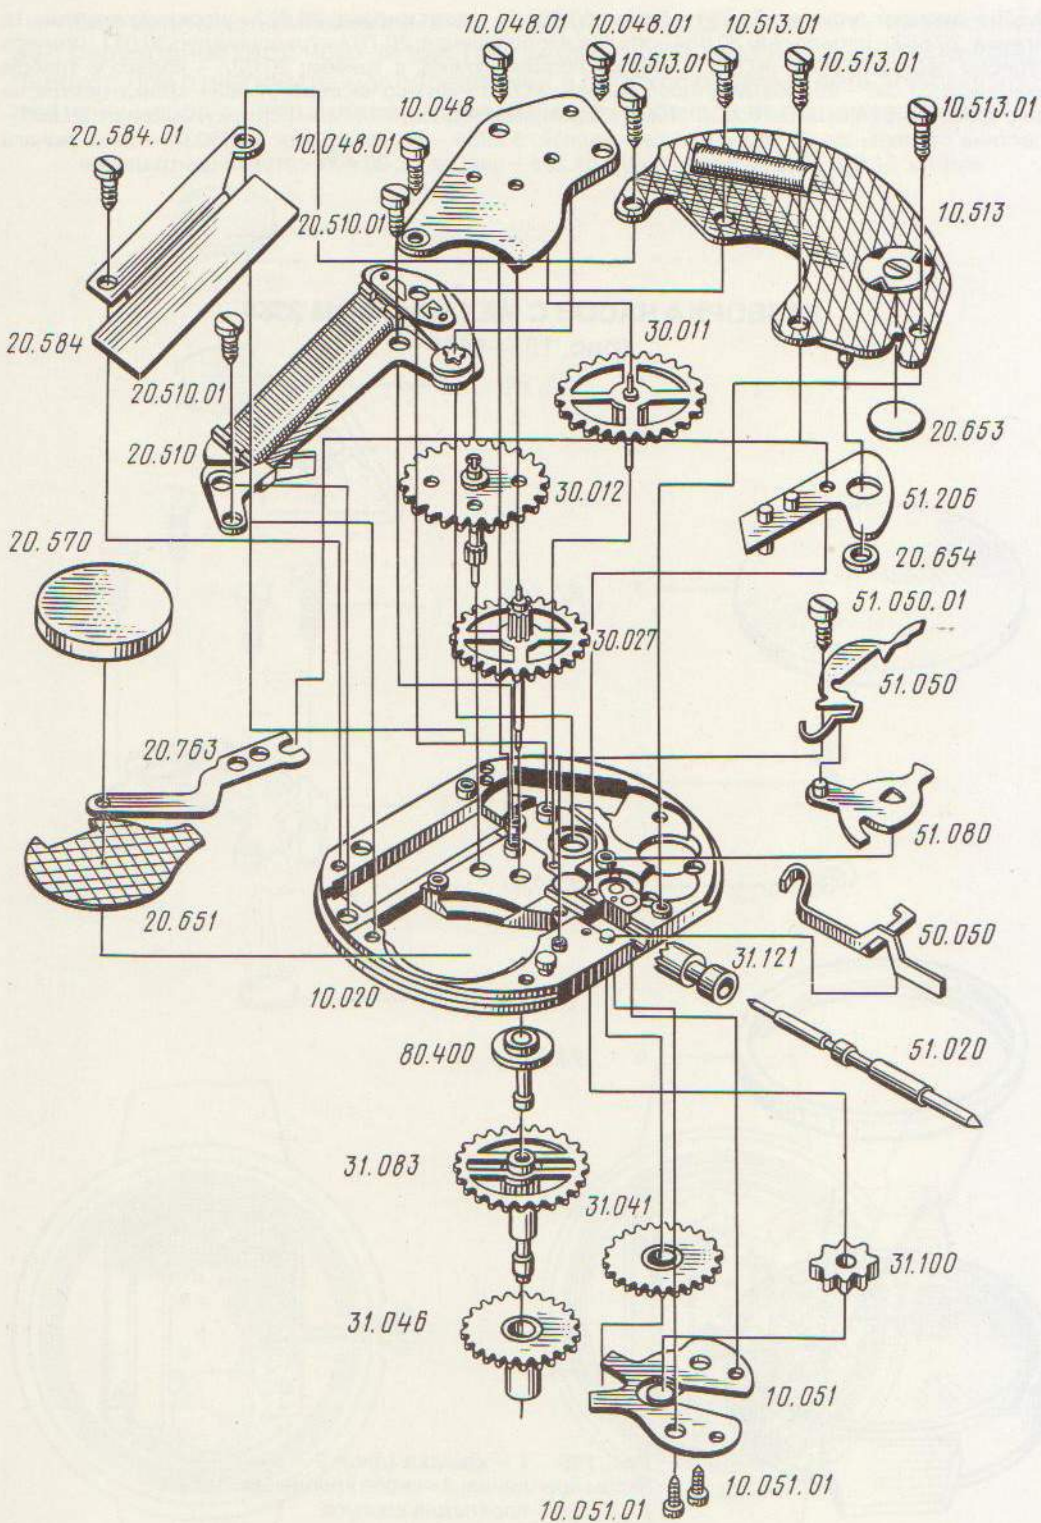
Детали и сборочные единицы механизма часов 2356:
